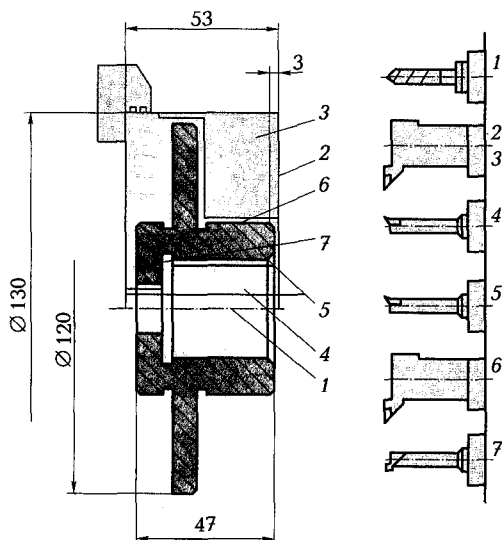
Типовая последовательность обработки с назначенной совокупностью режущих инструментов:
